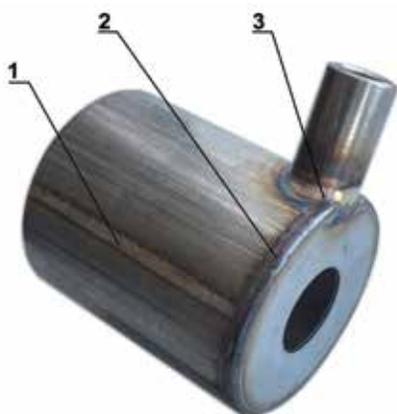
Внешний вид корпуса обогревателя: 1 – продольный шов обечайки, сваренный на установке АС411-С1; 2 – кольцевой шов соединения обечайки с доньшком, сваренный на установке АС399-С; 3 – круговой седловидный шов соединения обечайки с бонкой, сваренный на установке АС399-С4
